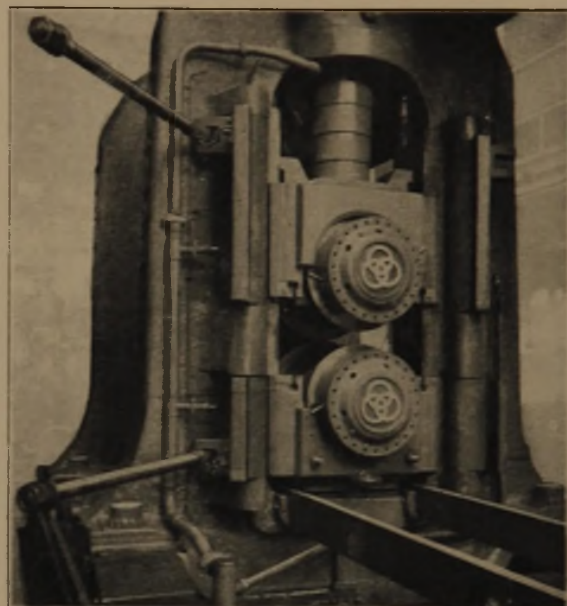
Blockgerüst mit axial einstellbarem Lager.
